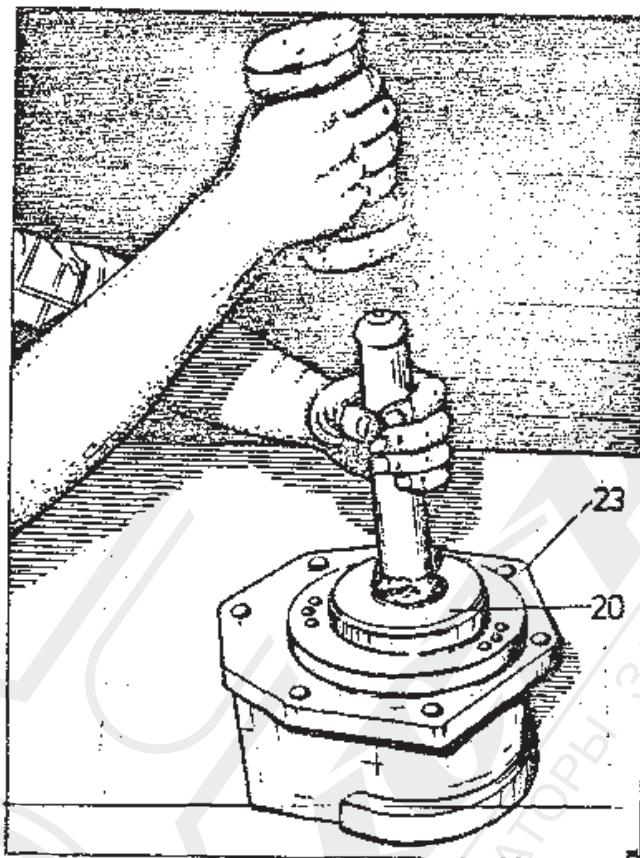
Вдавливание с помощью стержня внешнего кольца конусного роликоподшипника 20 в отверстие корпуса 23 до упора с установочным кольцом.
